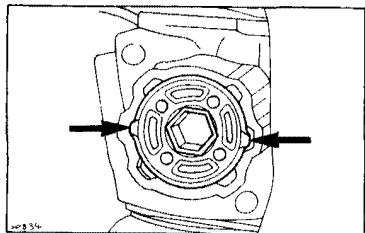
Стопорные лапки на регулировочной гайке упора рейки (указаны стрелками)
